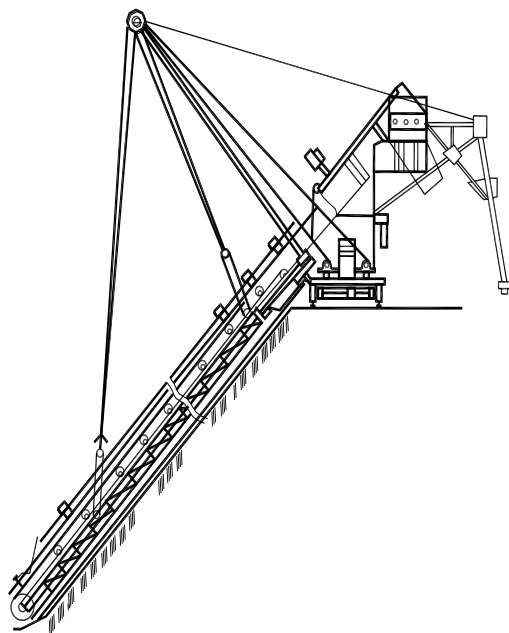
Конструктивная схема карьерного цепного экскаватора поперечного копания
